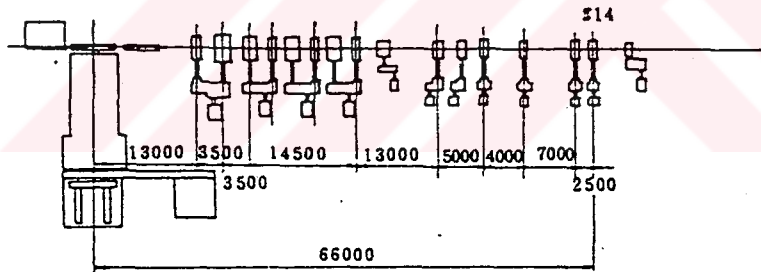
'da çok-yarma haddeleme planı ile konvansiyonel iki-kol haddeleme planı bir örnekle karşılaştırılır.
